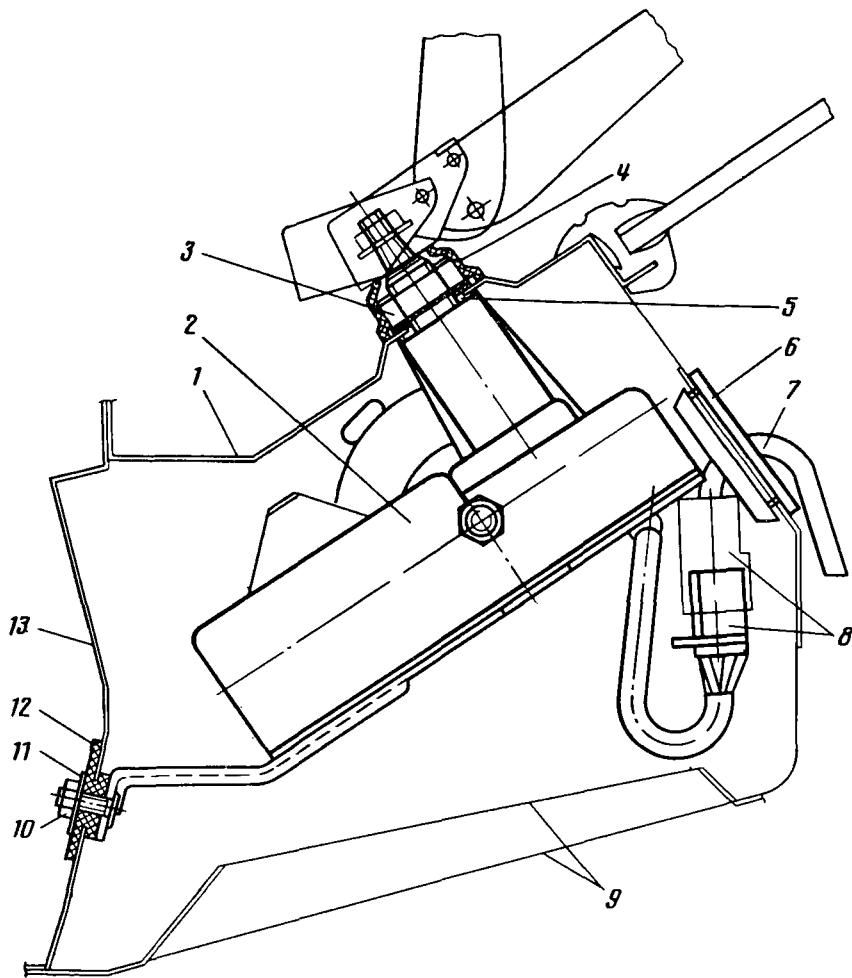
Установка на кузов моторредуктора (стеклоочистителя):
